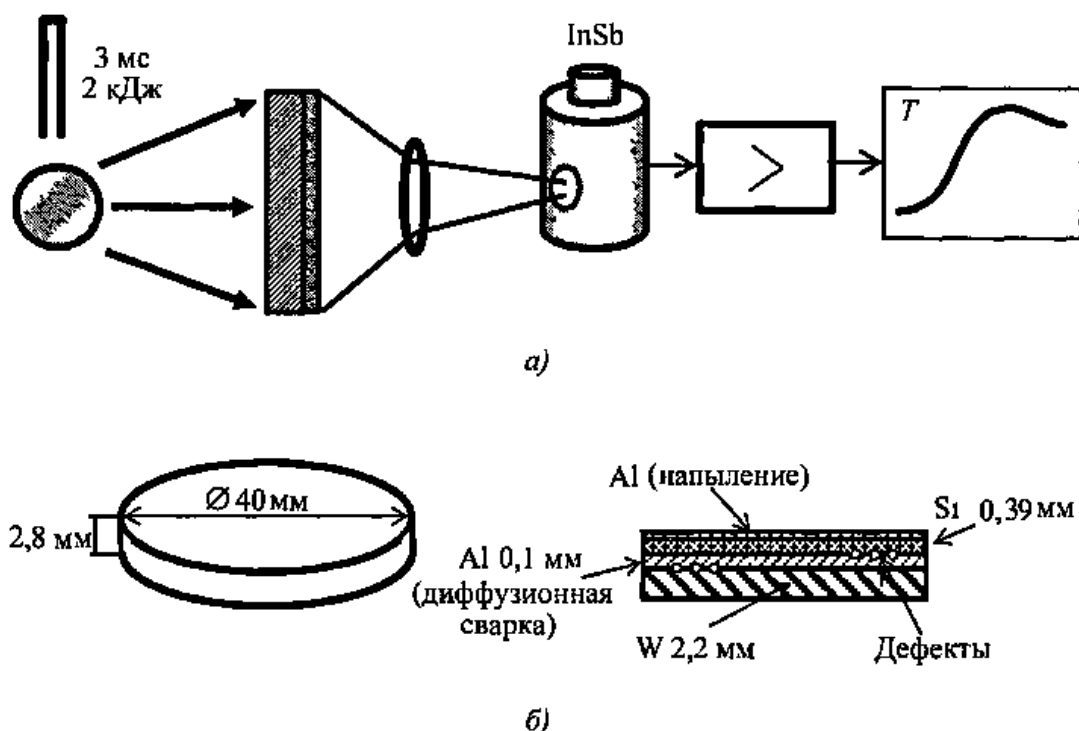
Активный ТК качества диффузионной сварки силовых ВЭ: а – схема двустороннего импульсного ТК, б – схема ВЭ
